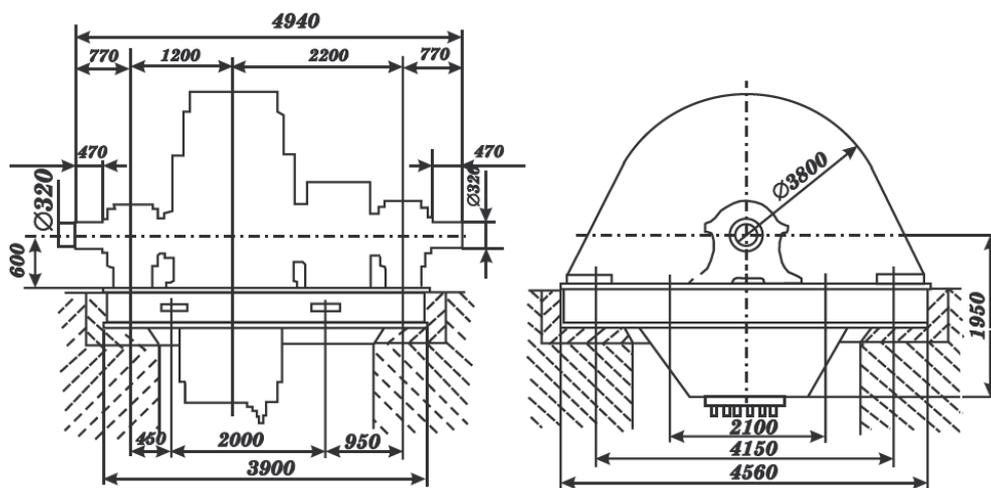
Габаритные, установочные, присоединительные размеры двигателя
